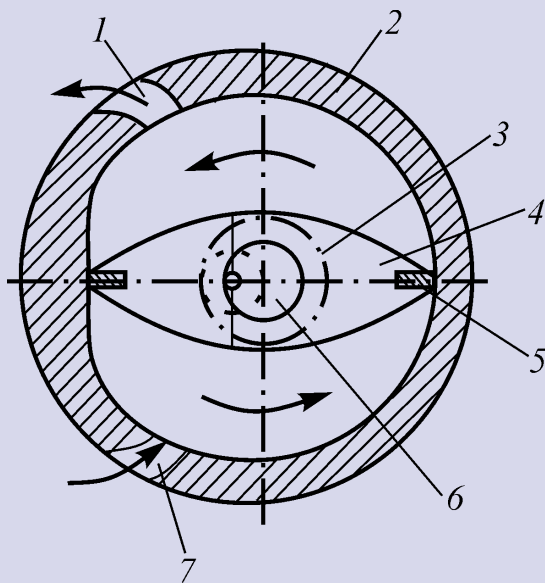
Схема роторно-поршневого компрессора с двухвершинным ротором: 1 — выпускное окно; 2 — корпус; 3 — зубчатая синхронизирующая передача внутреннего зацепления; 4 — ротор; 5 — радиальное торцевое уплотнение; 6 — эксцентриковый вал; 7 — впускное окно
